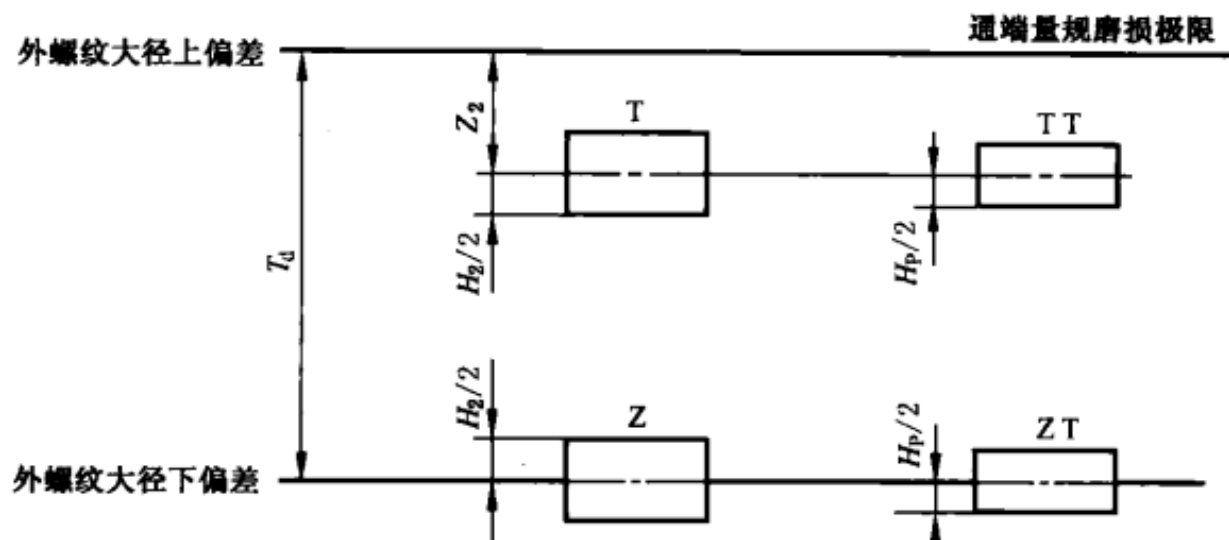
光滑环规或卡规直径的公差带位置
